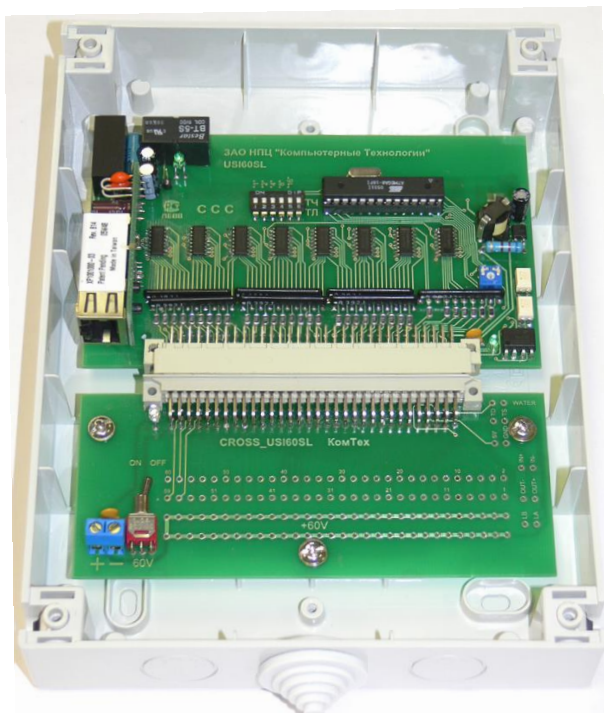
Общий вид устройства со снятой крышкой корпуса
